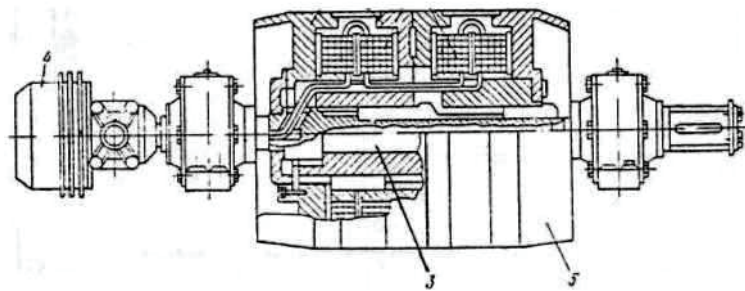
Электромагнитный шкив: 1 — диски-полюсы; 2 — катушка; 3 — вал; 4 — токораспределительная коробка; 5 — корпус шкива [5]
